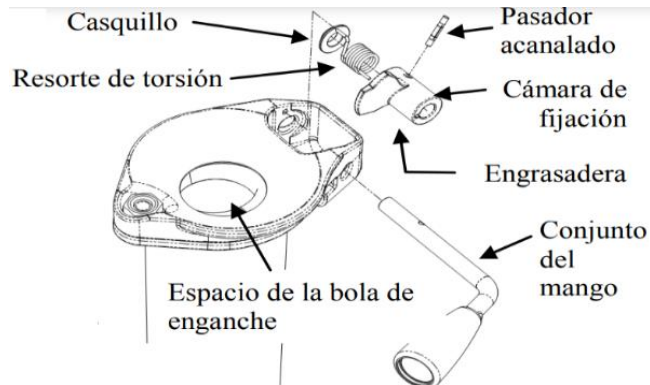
, Acoplador BX1 en despiece. Fuente: Manual acoplador bulldog.
